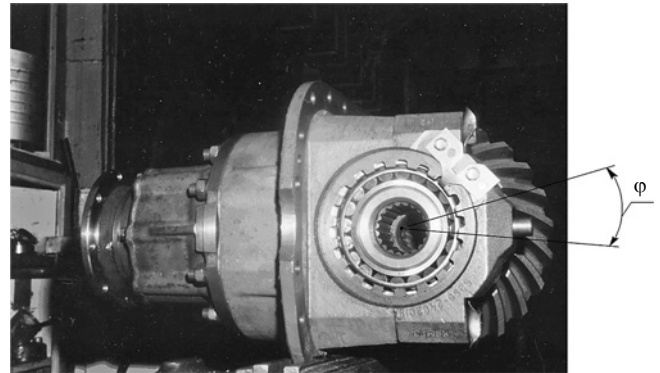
Гнездо подшипника дифференциала в сборе с резьбовым корончатый регулировочным кольцом и стопором
